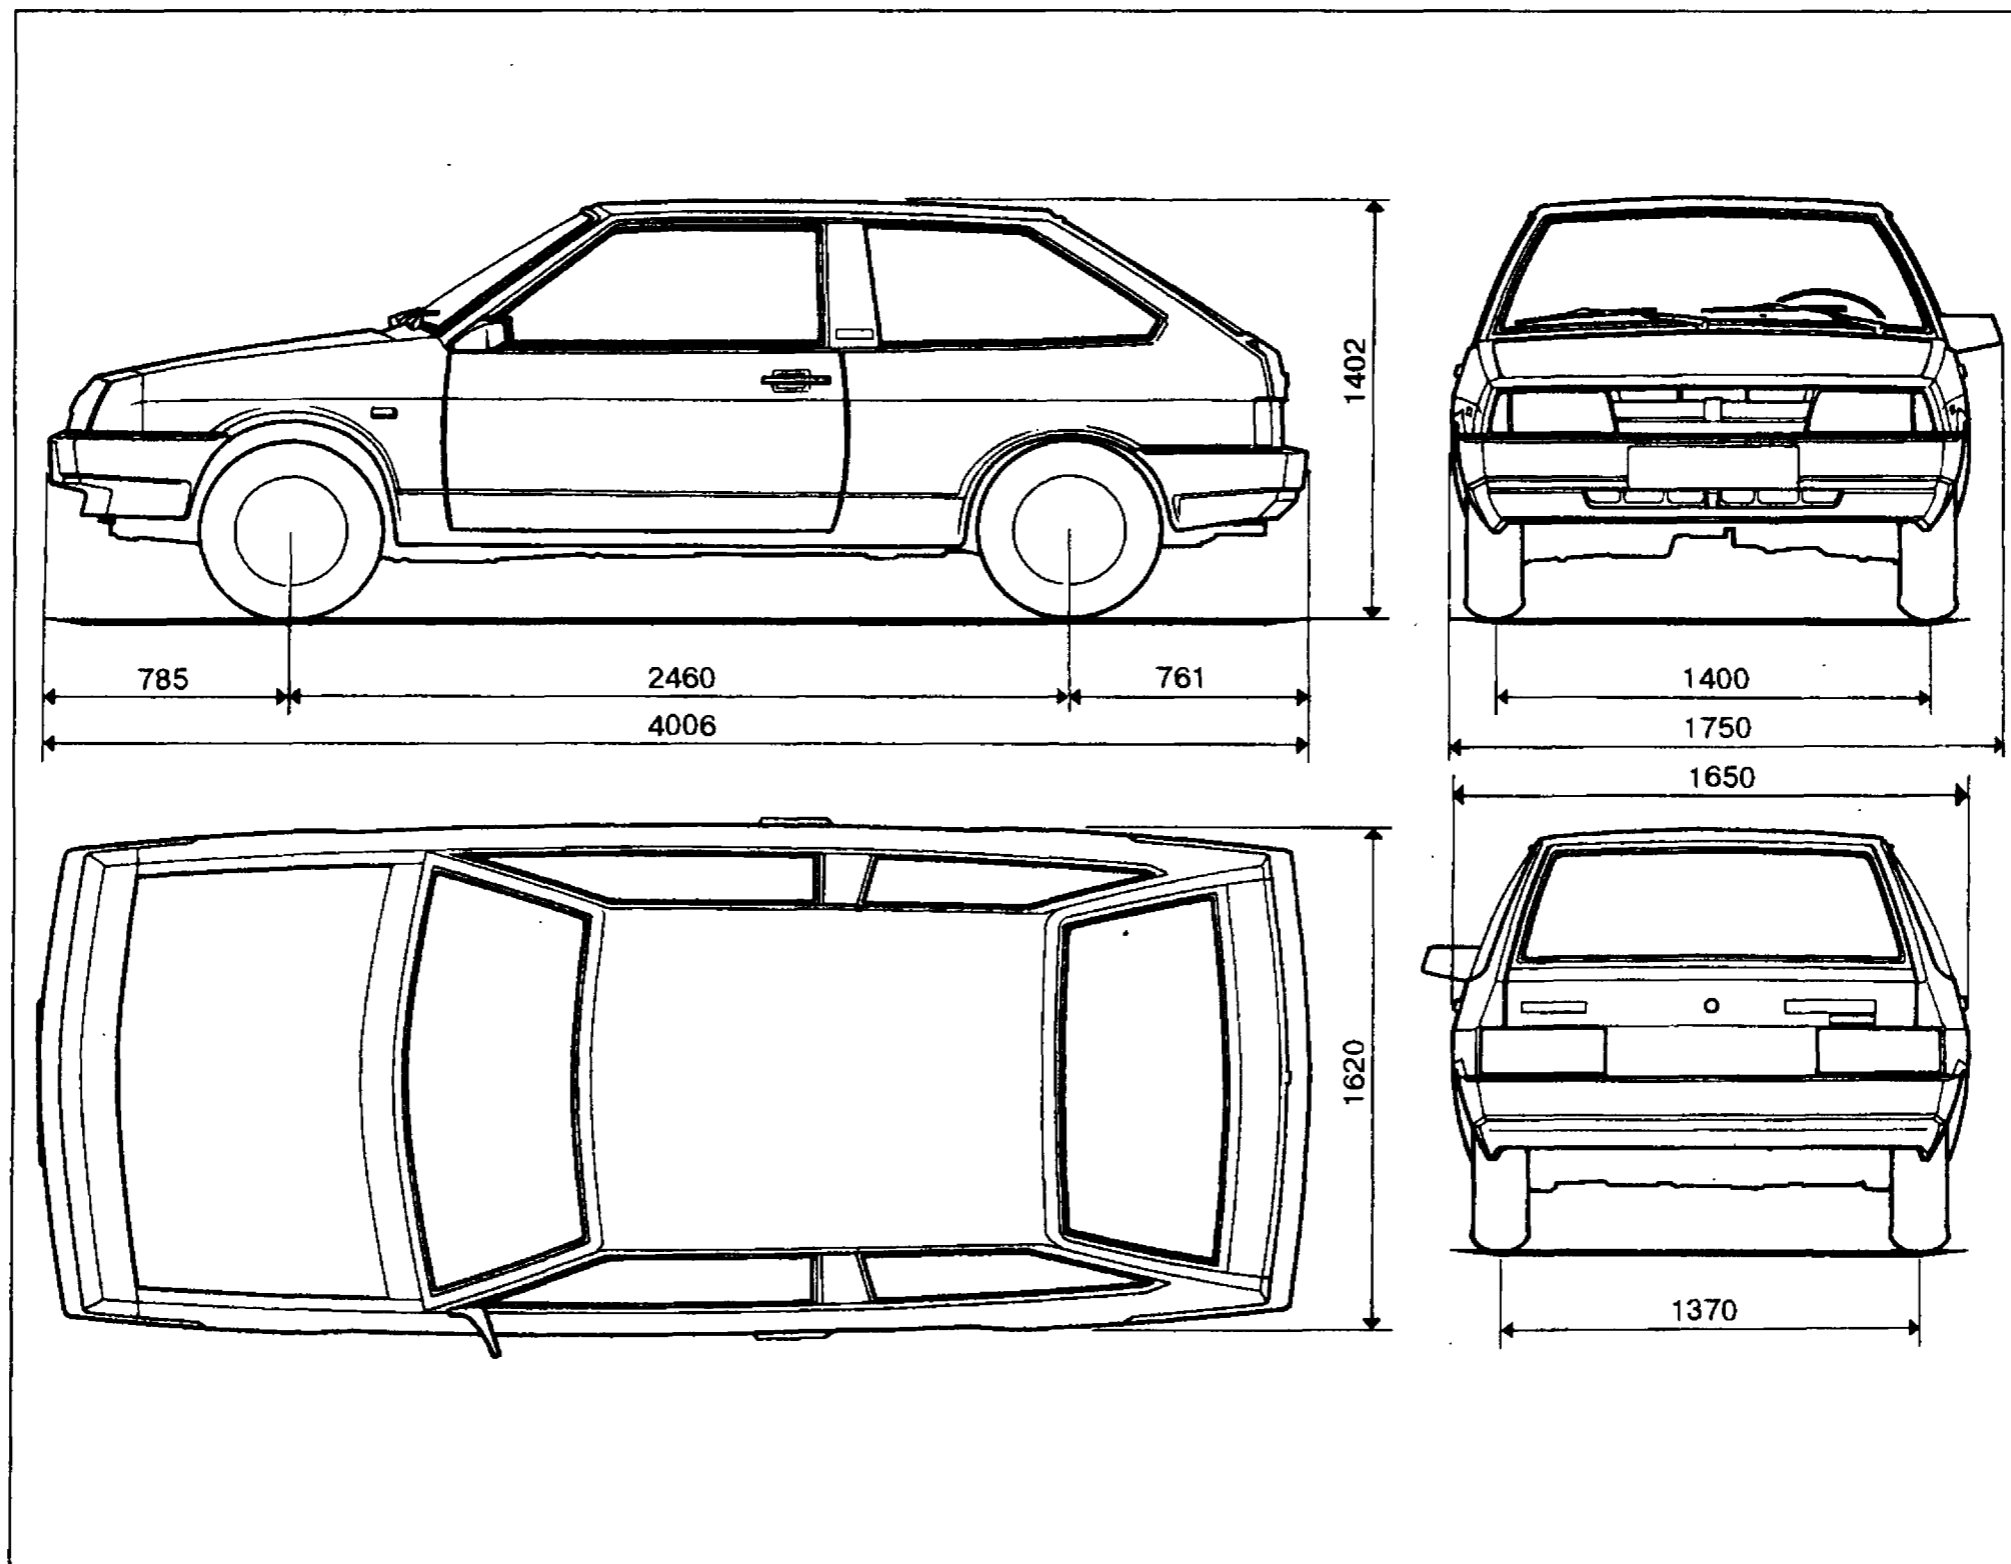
Габаритные размеры автомобиля ВАЗ-2108
